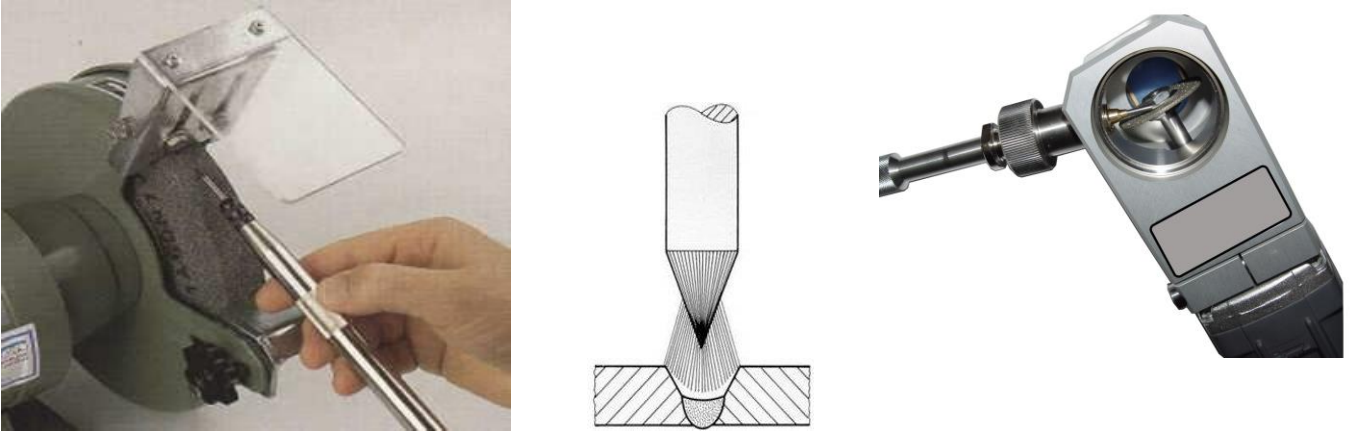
Doğru akım negatif kutuplama ile saf argon gazı kullanımında bilme açısına bağlı elde edilecek ark şekli ve nüfuziyet formu, AWS Welding Handbook Vol.2 Welding Process Part 1
